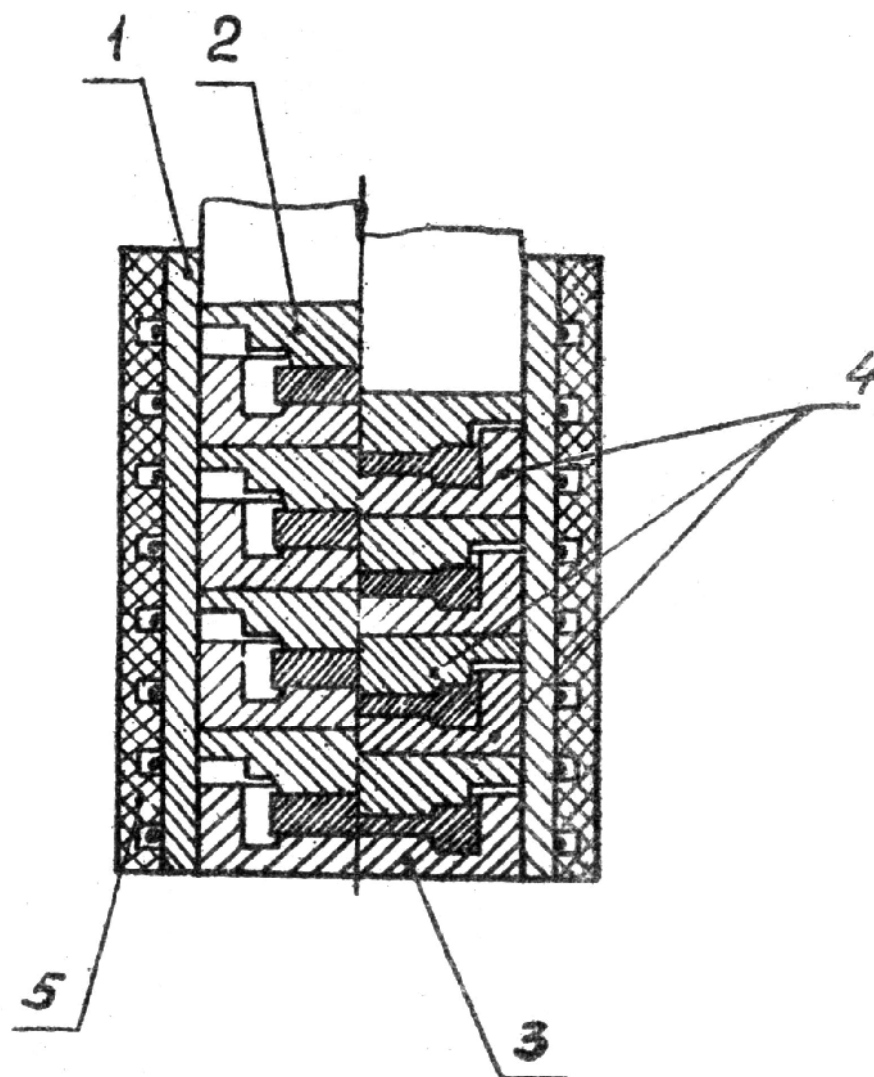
Инструмент для многослойной объемной штамповке четырех заготовок
